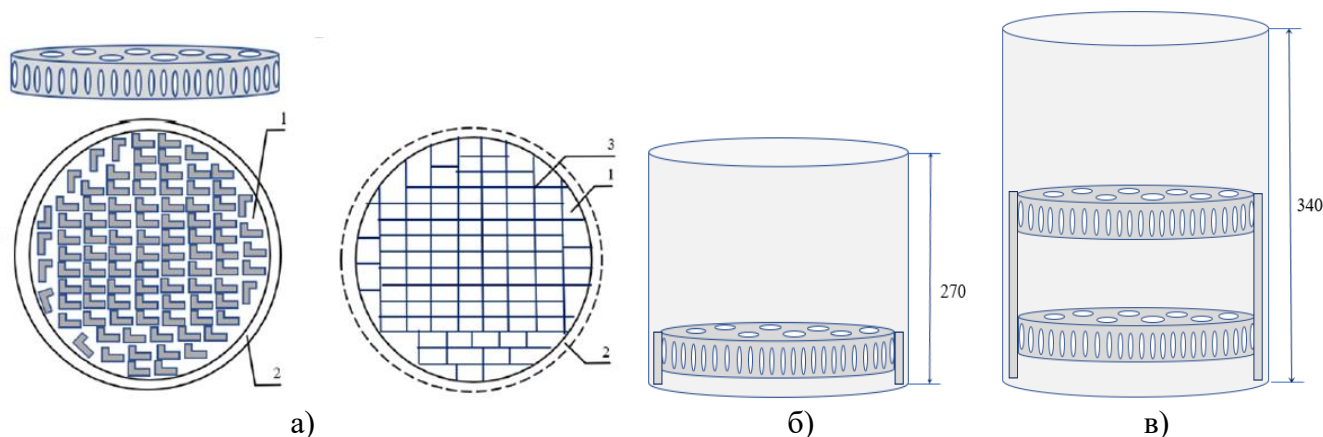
Схематическое изображение рационального варианта размещения деталей: а – базовая часть приспособления и сменная наладка; б – одноярусное приспособление; в – двухярусное приспособление.
